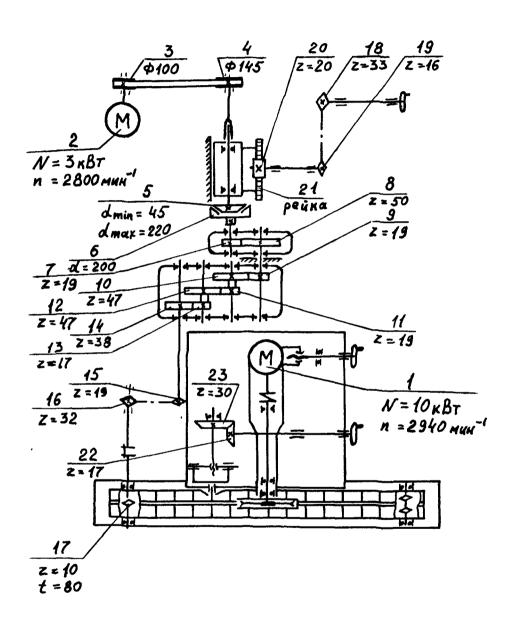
Кинематическая схема станка модели ЦДК4-3
